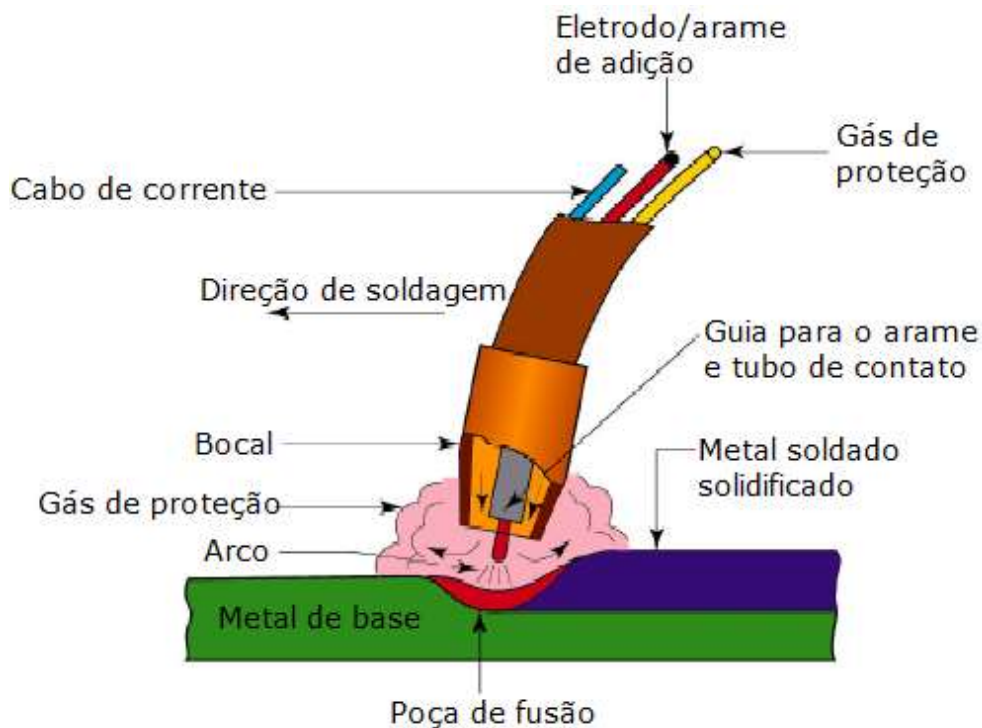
Esquema do processo de soldagem GMAW. Adaptado de [20].
